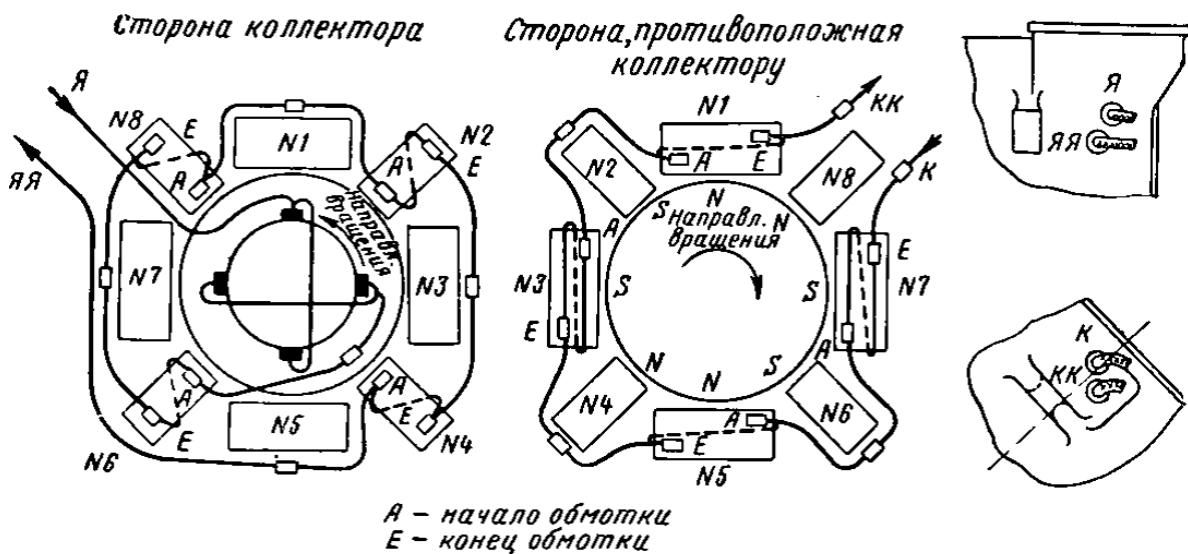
Схема соединения обмоток тягового двигателя НБ-406
